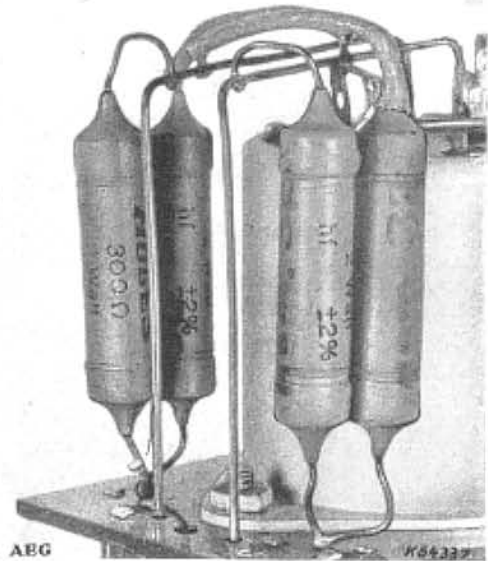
Gut ausgeführte Schweißung von Kupferdrähten untereinander.
